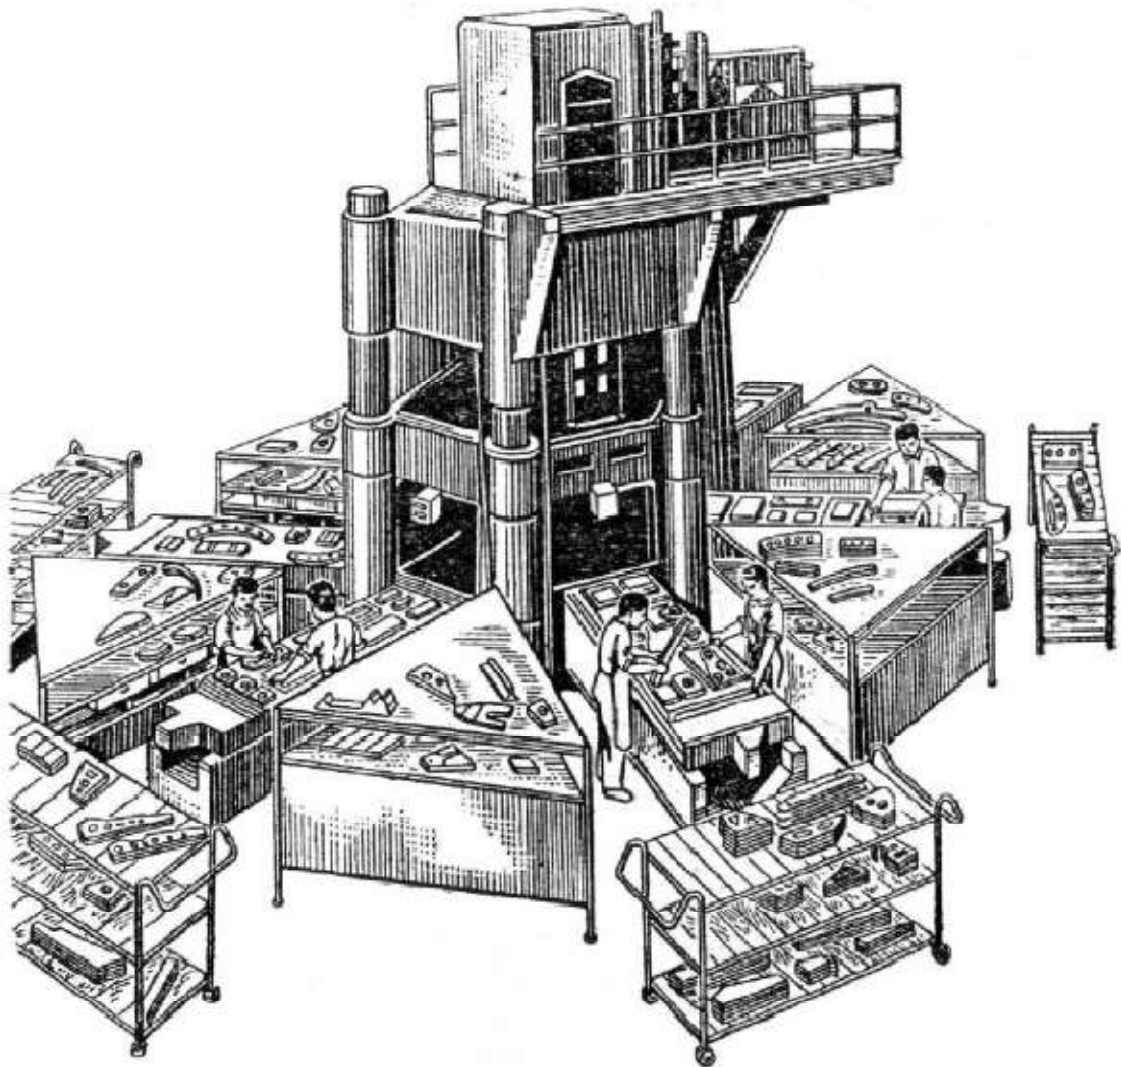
Планування гідравлічного пресу з 6 рухомими столами
